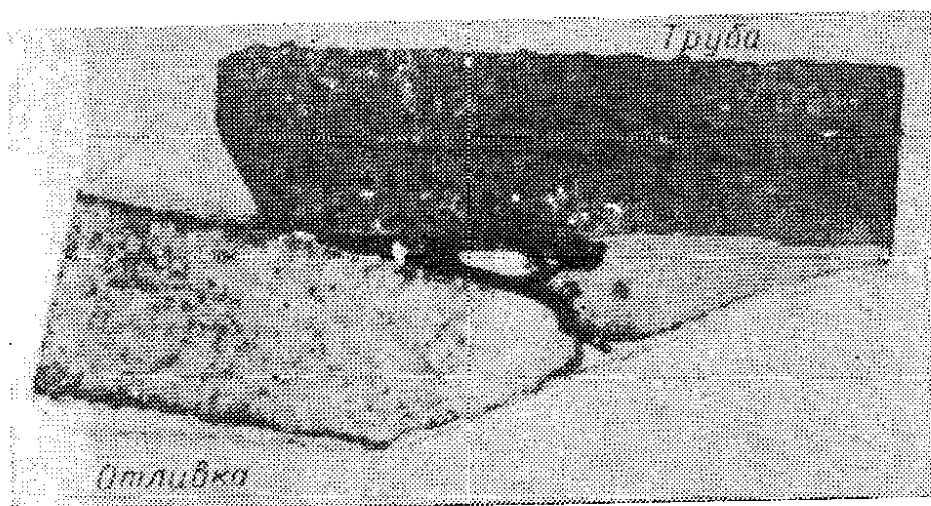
В сечении сварного шва, соединяющего трубу с правой отливкой, видны непровары (примерно в 1/3 величины)
